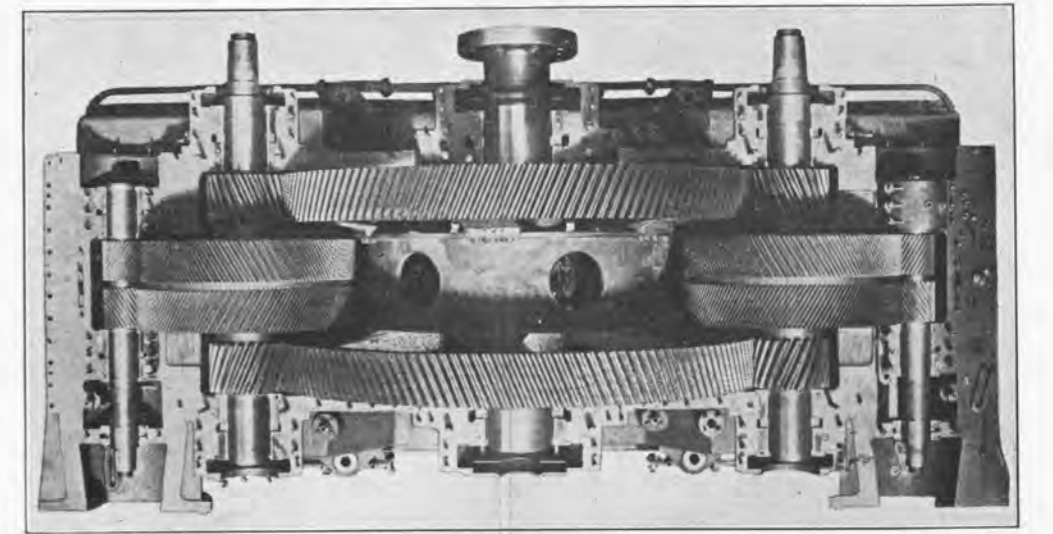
Dobbelt Gear fra to Turbineakser til en Skruesaksel.
